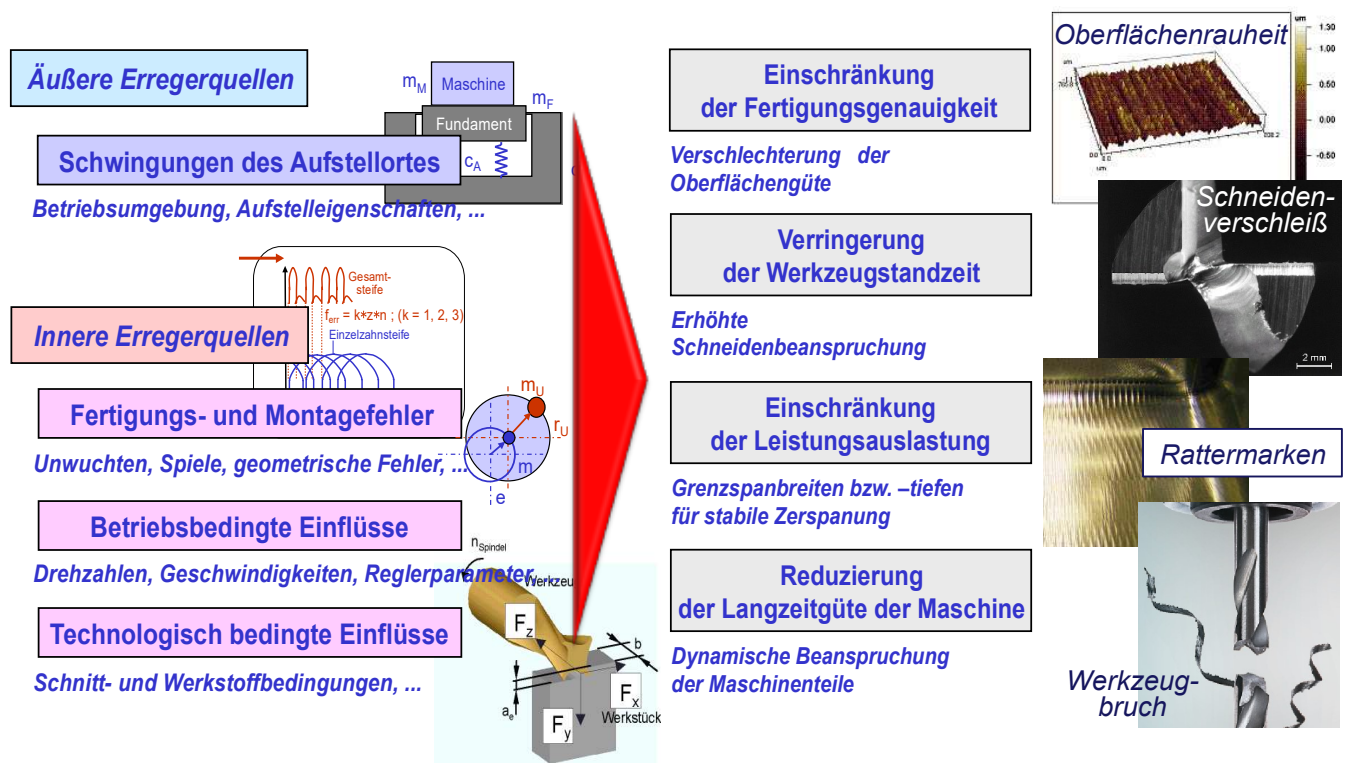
Auswirkungen von Schwingungen an Werkzeugmaschinen
